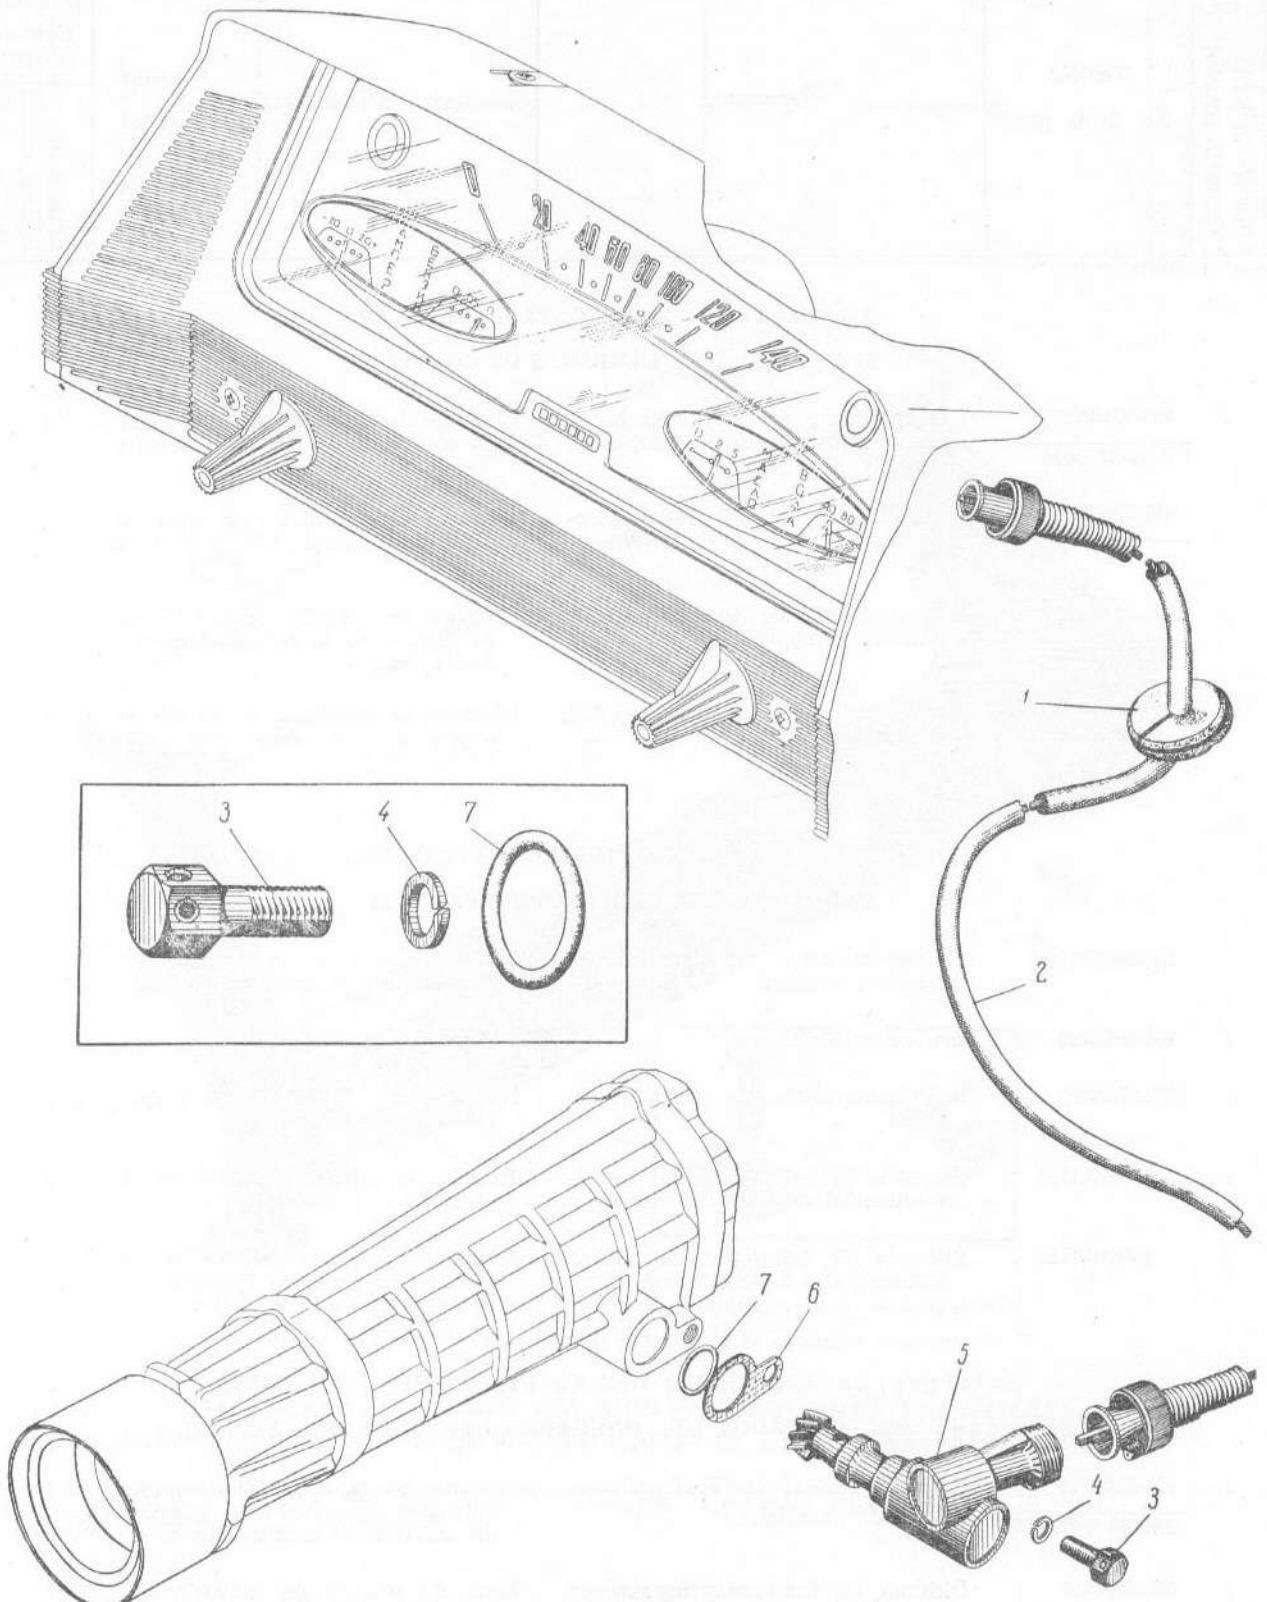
Geschwindigkeitsmesser mit biegsamer Antriebswelle
